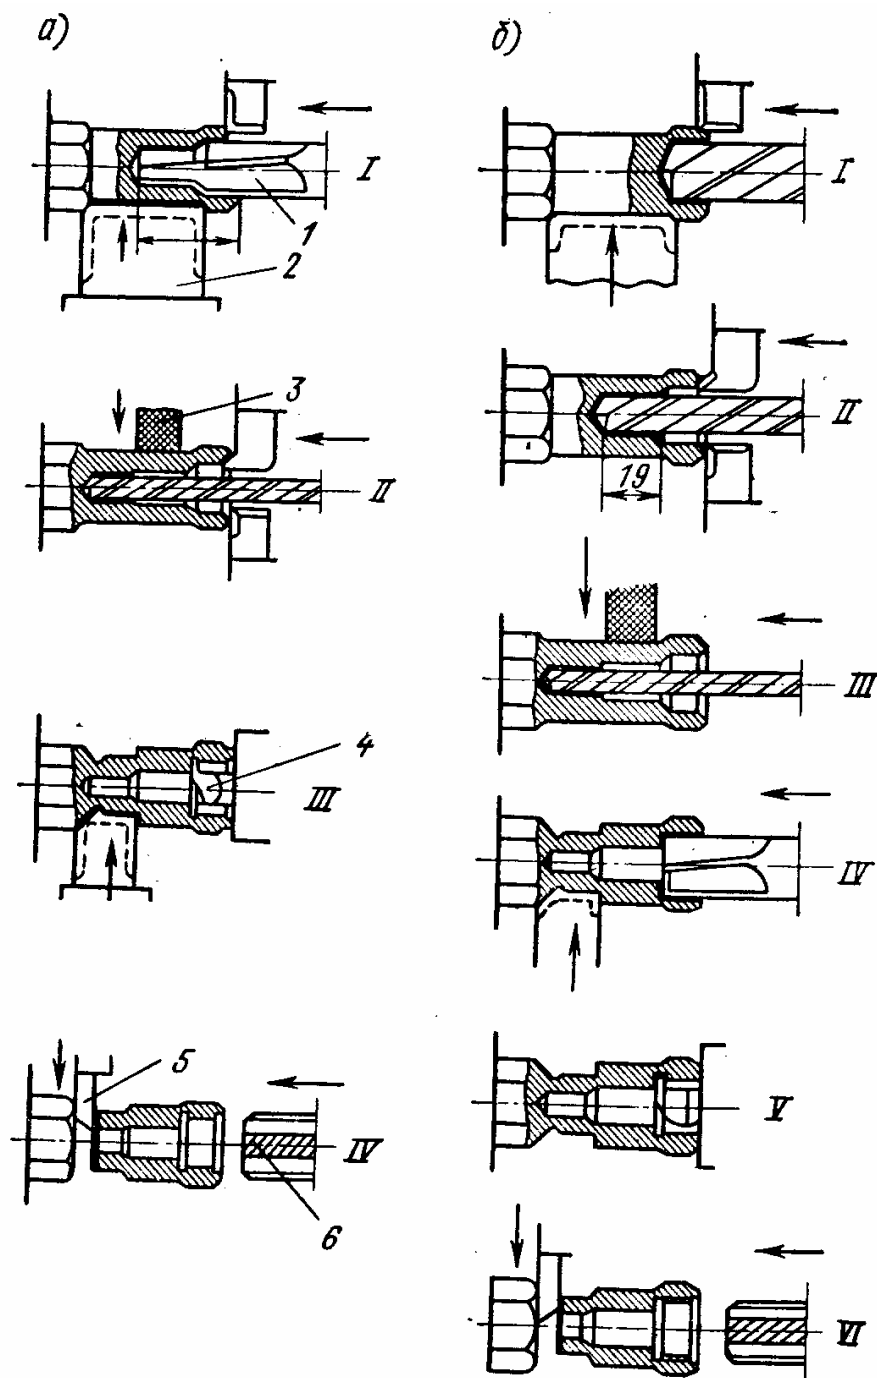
Наладка четырех- и шестишпиндельного автомата для обработки корпуса свечи двигателя: *а* – наладка для четырех шпинделей; *б* – наладка для шести шпинделей; *I-IV* и *I-VI* – номера шпинделей. Стрелки указывают направление подачи
